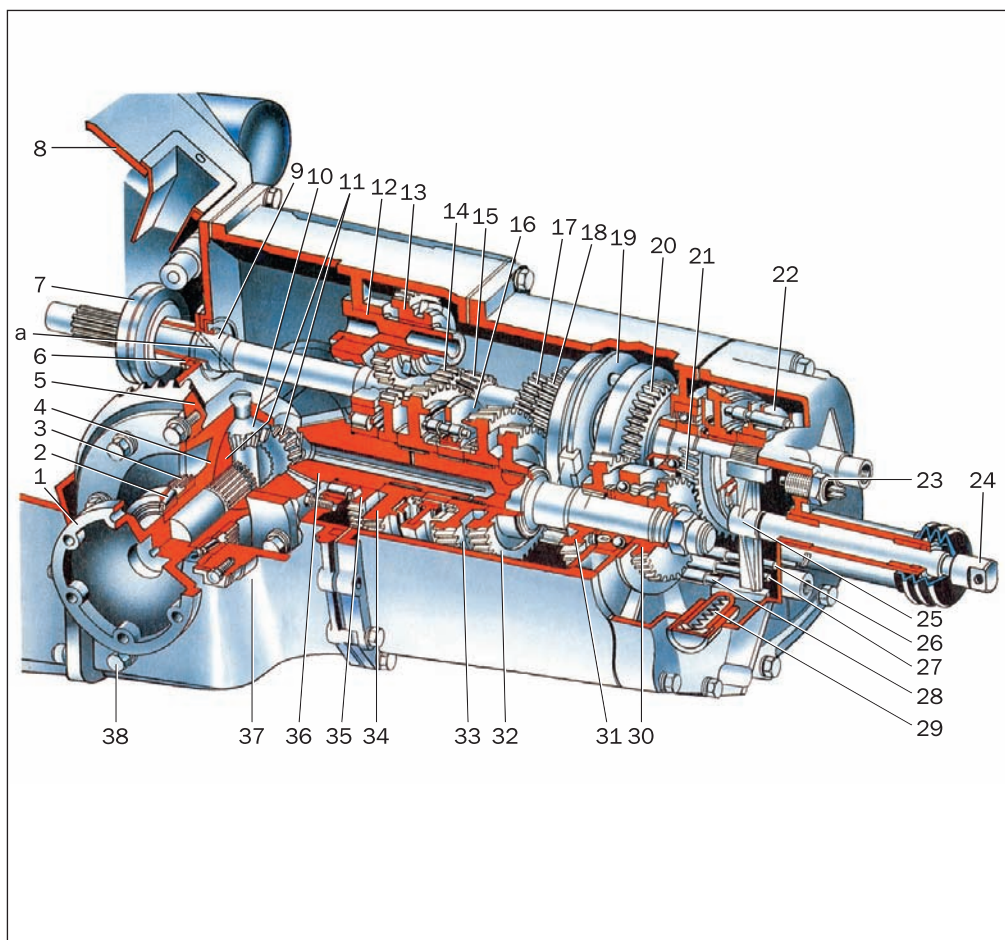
Конструкция двухвальной пятиступенчатой коробки передач при переднем приводе и продольном расположении двигателя (Москвич-2141): 1 — фланец полуоси; 2 — подшипник дифференциала; 3 — ведущая шестерня редуктора привода спидометра; 4 — коробка дифференциала; 5 — ведомая шестерня главной передачи; 6 — манжета (сальник); 7 — подшипник выключения сцепления; 8 — картер сцепления; 9 — первичный вал; 10 — сателлит; 11 — полуосевые шестерни; 12 — ось промежуточной шестерни заднего хода; 13 — промежуточная шестерня заднего хода; 14 — шестерня передачи заднего хода первичного вала; 15 — шестерня I передачи первичного вала; 16 — синхронизатор I и II передач; 17 — шестерня II передачи первичного вала; 18 — ведущая шестерня III передачи; 19 — синхронизатор III и IV передач; 20 — ведущая шестерня IV передачи; 21 — ведущая шестерня V передачи; 22 — синхронизатор V передачи; 23 — выключатель света заднего хода; 24 — вал переключателя передач; 25 — переключатель передач; 26 — шток вилок переключения V передачи и заднего хода; 27 — шток вилок переключения III и IV передач; 28 — шток вилок включения I и II передач; 29 — плунжер; 30 — ведомая шестерня V передачи; 31 — ведомая шестерня IV передачи; 32 — ведомая шестерня III передачи; 33 — ведомая шестерня II передачи; 34 — ведомая шестерня I передачи; 35 — ведомая шестерня заднего хода; 36 — ведущая шестерня главной передачи; 37 — картер главной передачи; 38 — пробка маслосливного отверстия; а — отверстие-сапун
